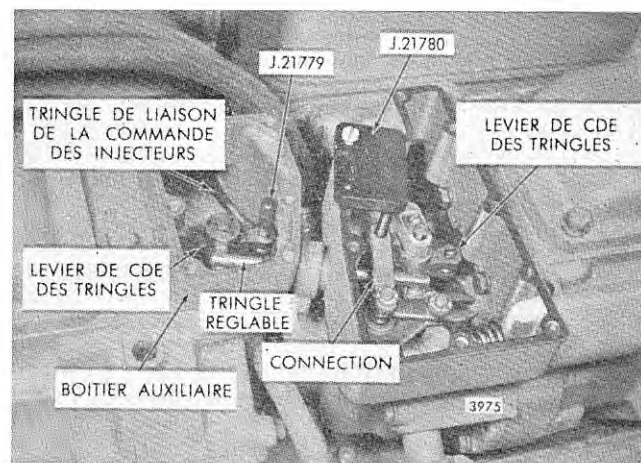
V-2 - Mise en place des jauges de réglage J21779 et J21780
